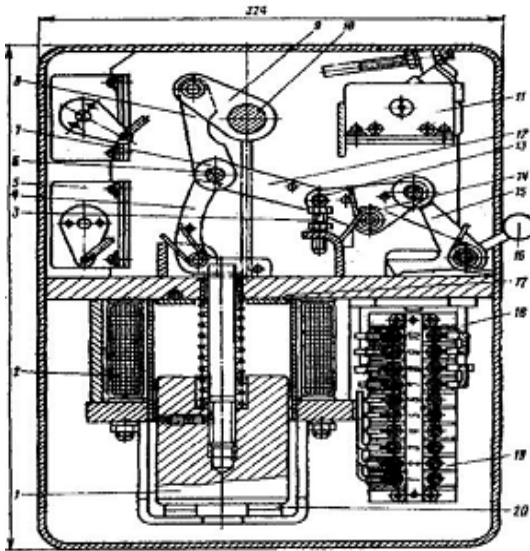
Устройство электромагнитного провода ПЭ-11 1-Магнитопровод; 2- катушка; 3-регулирующий винт; 4- удерживающая защелка 5-и 11-сигнально-блокировочные и быстродействующие вспомогательные контакты : 6 и 13-оси; 7- ролик; 8,9,12 и 14-рычаги ; 10-вал привода; 15-«собачка»; 16-рукоятка (кнопка) отключения ;17 – шайба; 18 – отключающие электромагнит; 19- контактодержатель ;20- резиновые прокладки.
